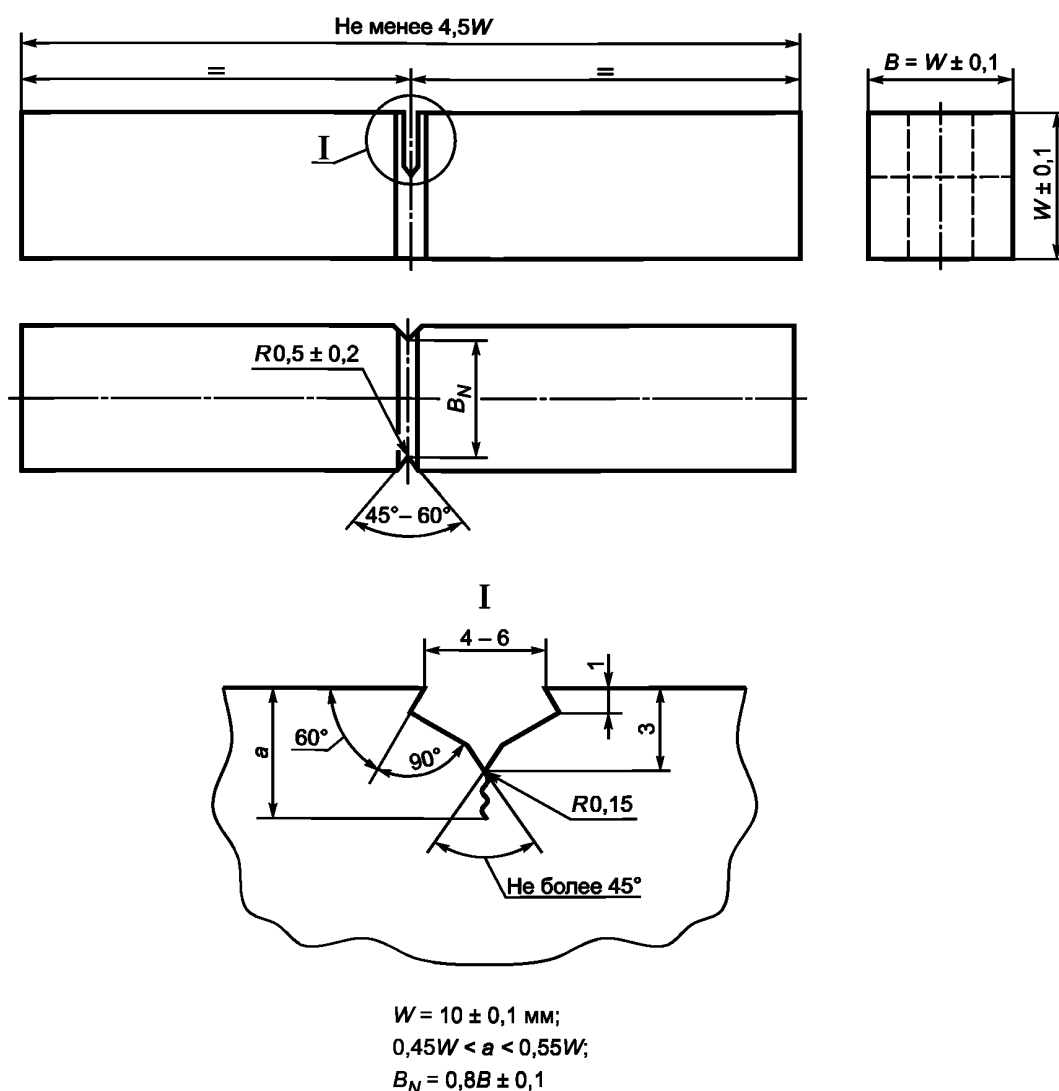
Образец типа Шарпи с трещиной, с боковыми канавками стандартной глубины (SE(B)-10/SG20)
